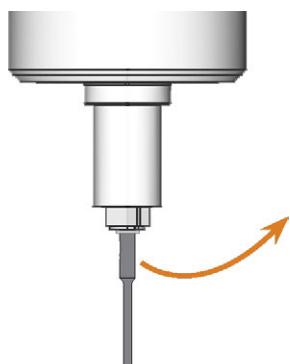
RETIRER L'OUTIL DE LA PINCE DE SERRAGE
